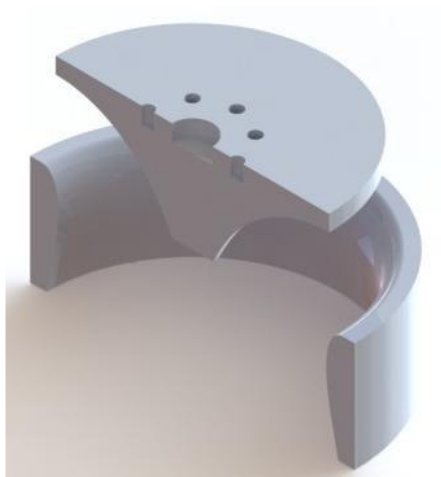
Vista isométrica em corte da coroa interna e externa do rotor.
